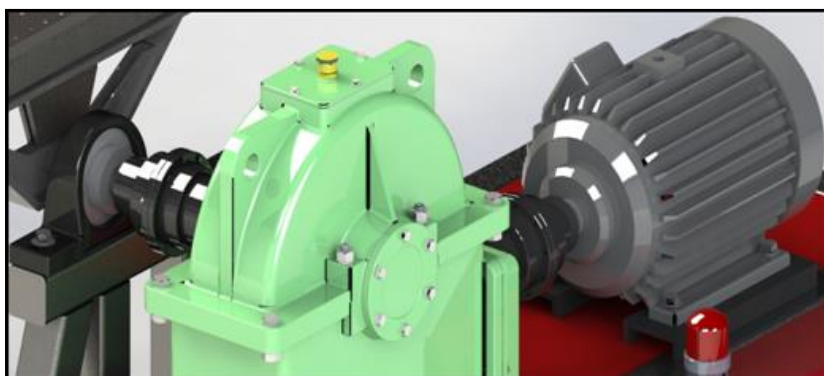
Conjunto motor-redutor acoplado ao eixo de transmissão.
